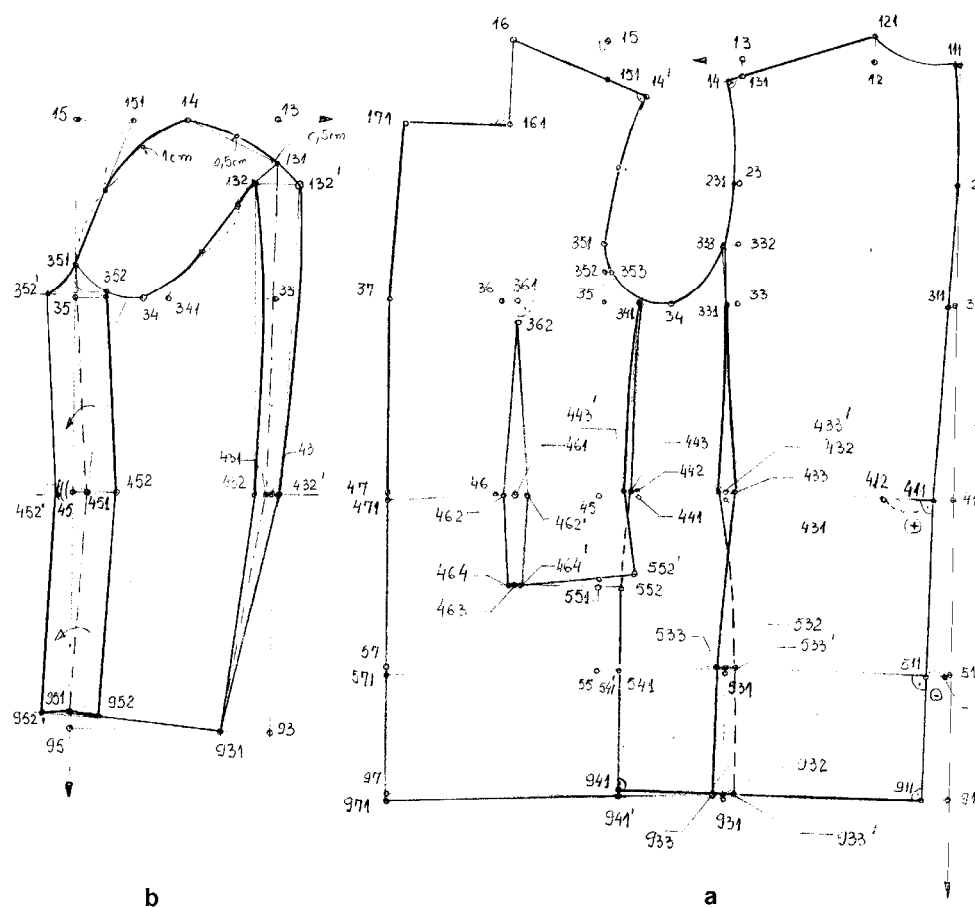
Construcția tiparelor de bază pentru produsul „Sacou pentru bărbați”:
